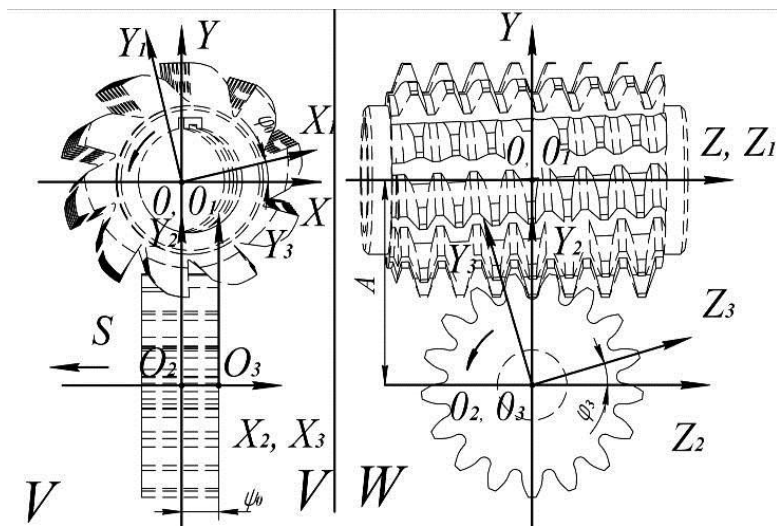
Схема зубофрезерування черв’ячною фрезою
